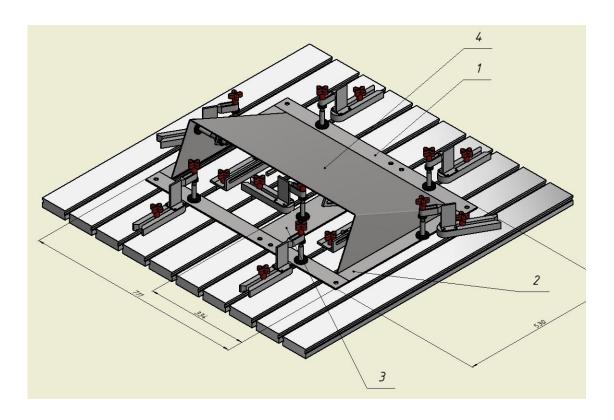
Модель кожуха котла KB-PM-1 в сборочном приспособлении
